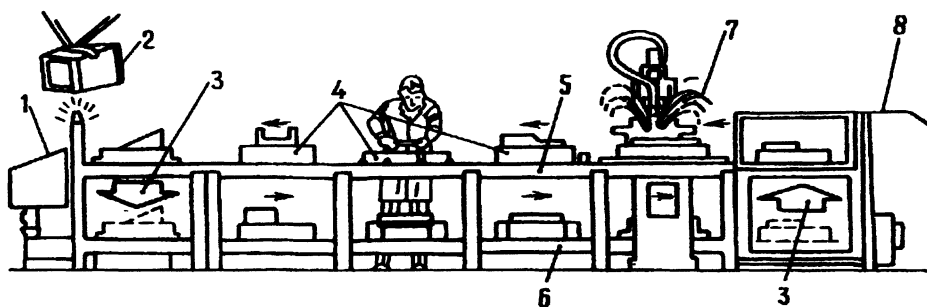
Гибкая производственная система для дуговой сварки (фирма Вествуд, Великобритания):
